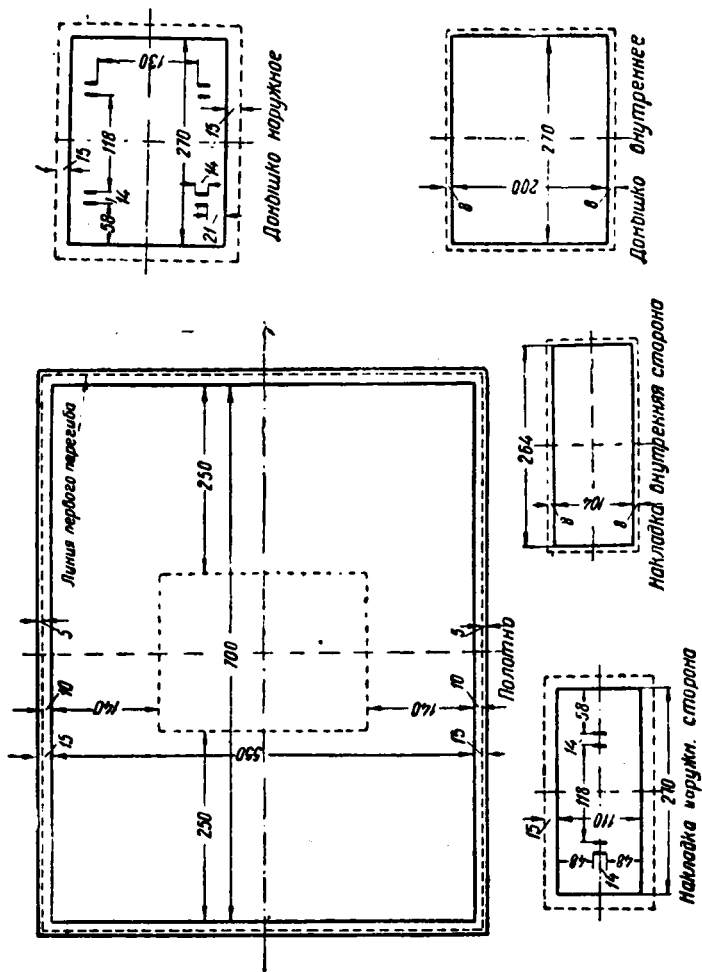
Чертеж деталей книгоноски размером 55 × 70 см
